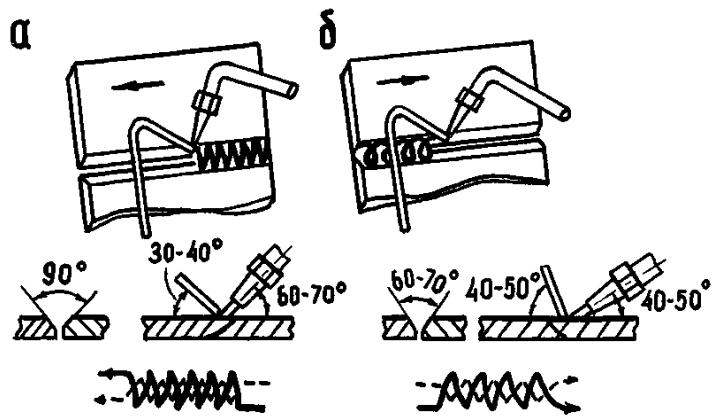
Способы сварки: а–левый; б–правый
